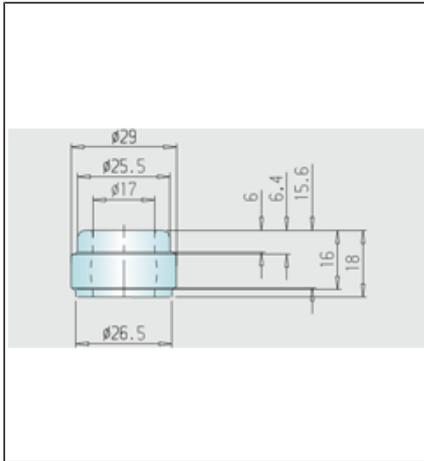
Mundstück für Korkenverschleißer nach DIN EN 12726
